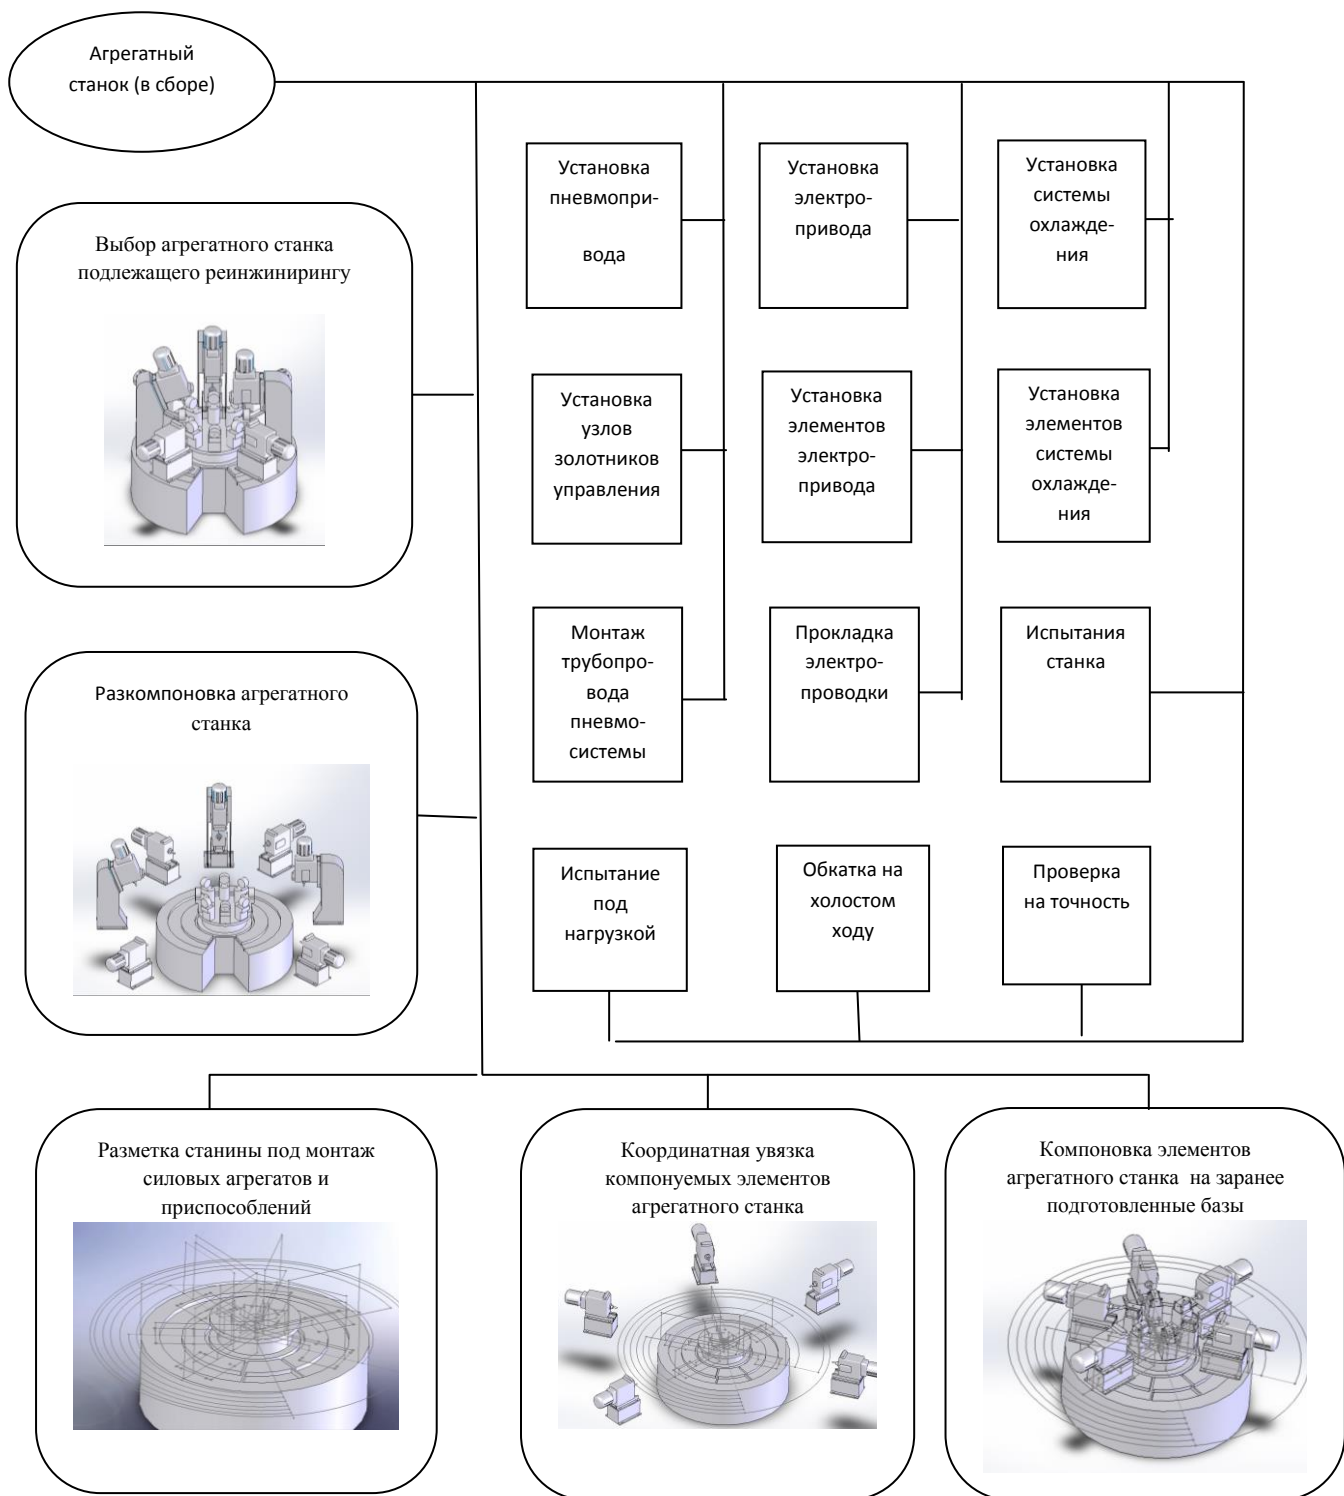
Схема сборки агрегатного станка при реинжиниринге.
